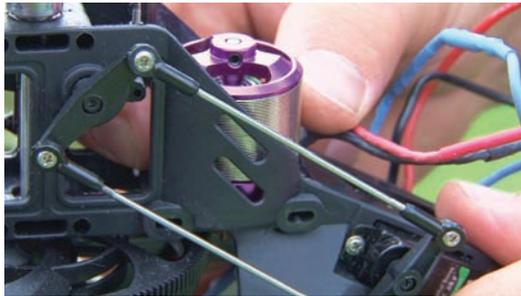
Zum Teil sind die Rahmen mit Langlöchern ausgestattet, sodass der Motor und die Montageplatte zum Einstellen des Zahnflankenspiels nur vor- oder zurückgeschoben werden müssen.
